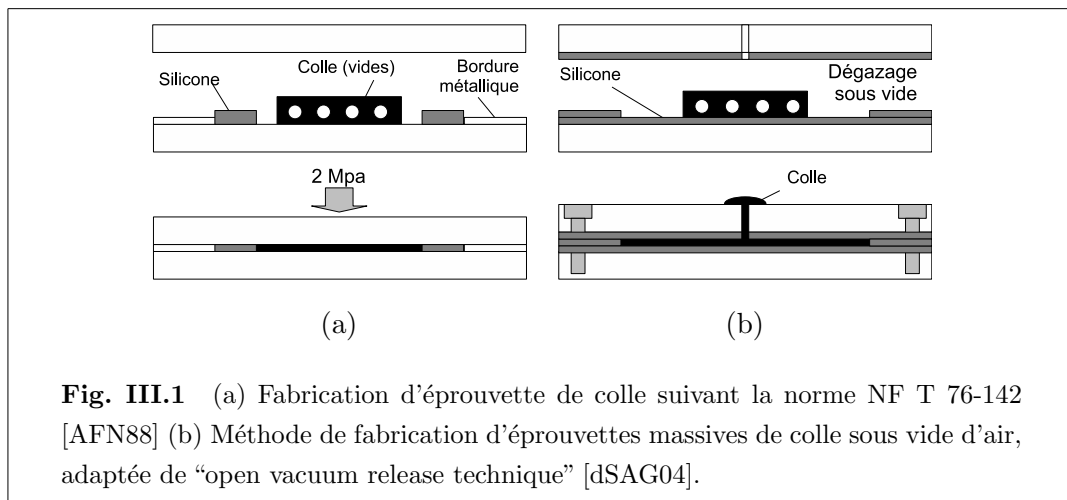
(a) Fabrication d'éprouvette de colle suivant la norme NF T 76-142 [AFN88] (b) Méthode de fabrication d'éprouvettes massives de colle sous vide d'air, adaptée de "open vacuum release technique" [dSAG04].
